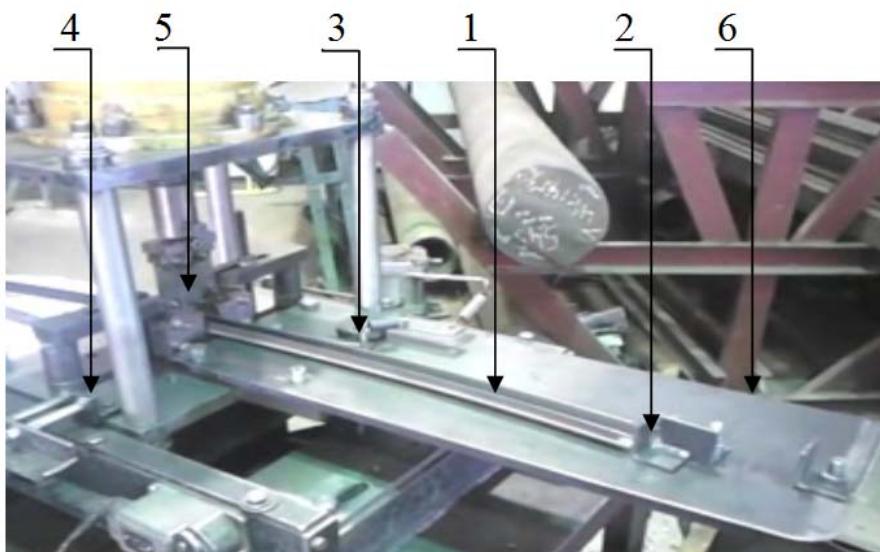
Пресс пневматический: 1 – профиль, 2 – упор, 3 – сбрасывающий механизм, 4 – каретка, 5 – штамп отрубной, 6 – платформа
